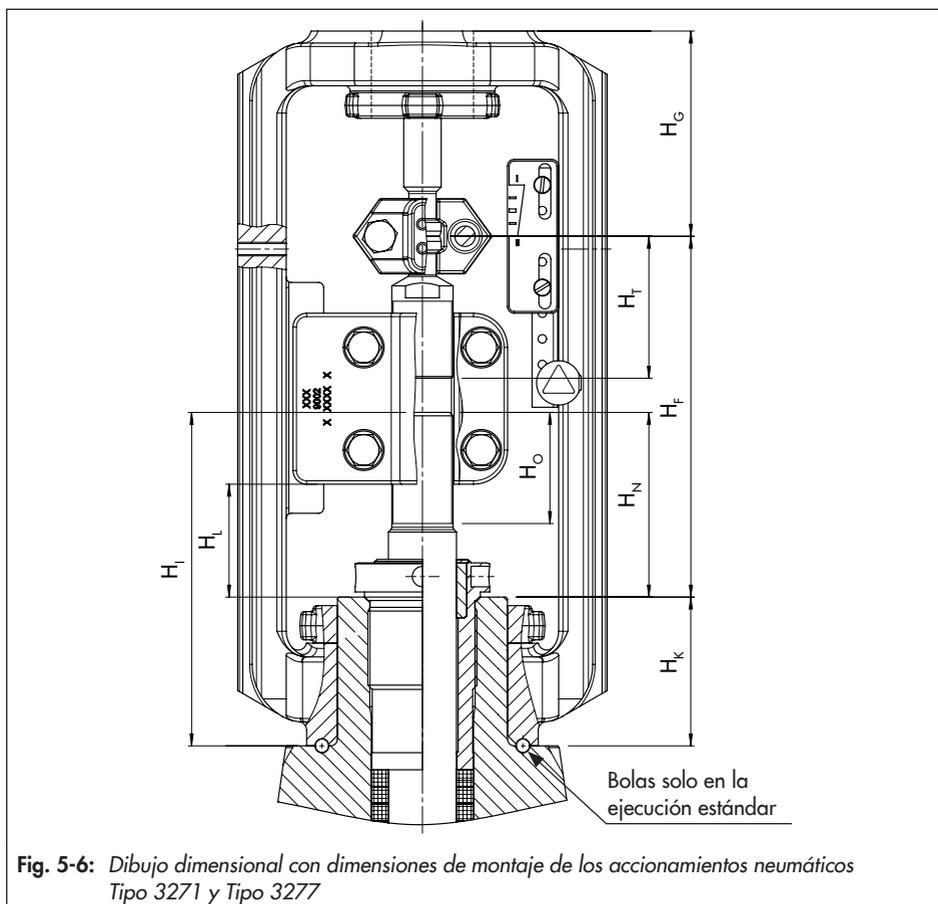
Dibujo dimensional con dimensiones de montaje de los accionamientos neumáticos Tipo 3271 y Tipo 3277
